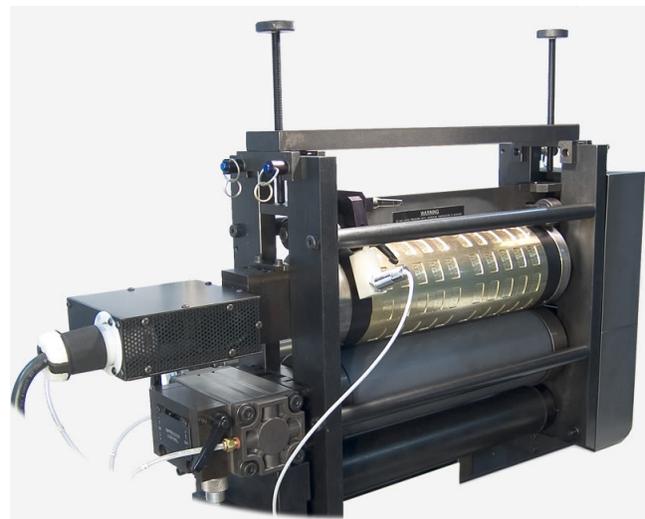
Máquina para impresión en Caliente (*Hot Stamping*)
